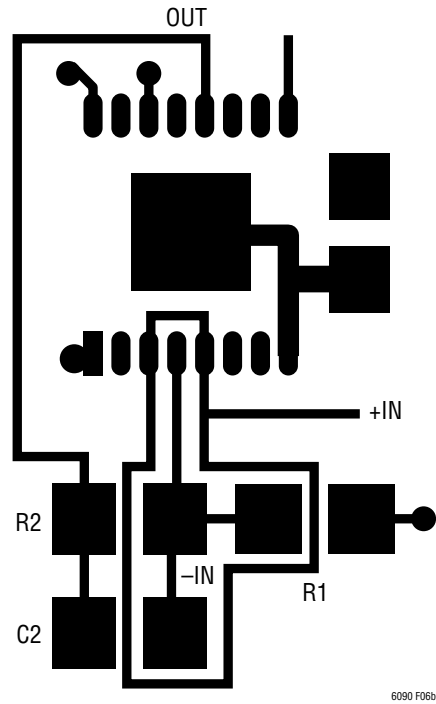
：具有保护环的 TSSOP 封装 PCB 布局
